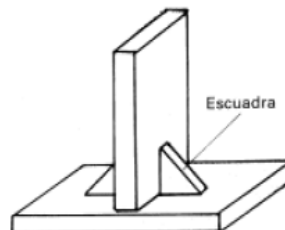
Elemento estructural de tipo escuadra ²⁵
